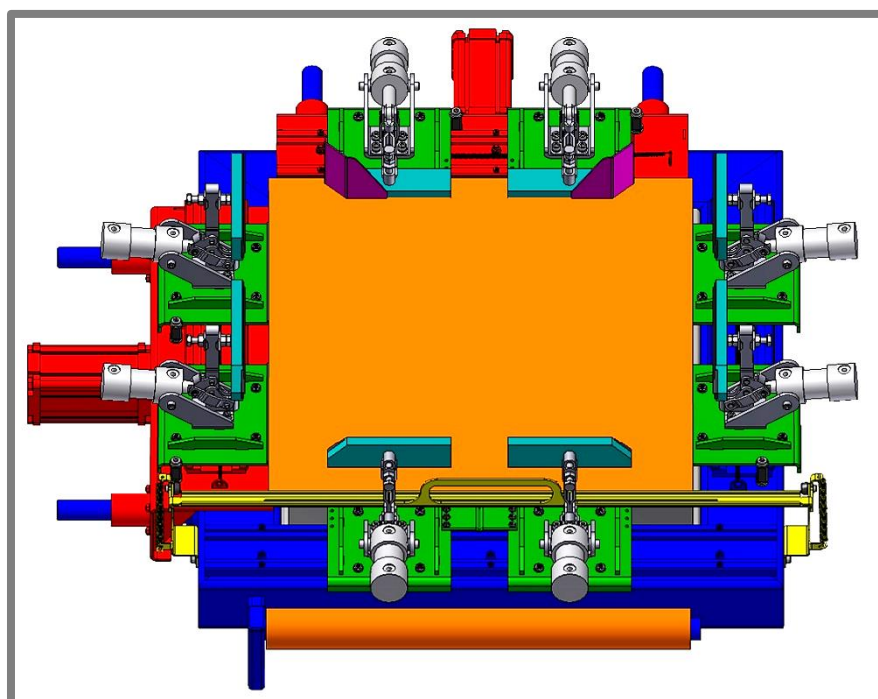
4. krok – umístění a zajištění tkaniny horními pneumatickými rychloupínkami
